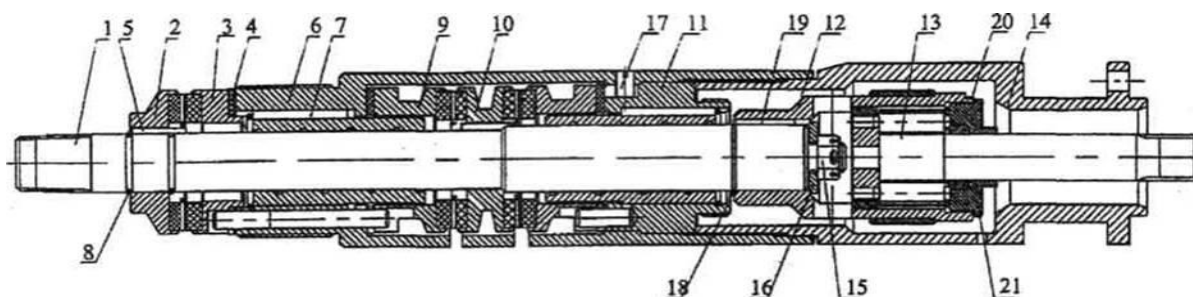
Основание: 1 - вал; 2 - обойма; 3 - обойма; 4 - кольцо; 5 - шпонка; 6 – корпус основания; 7 - шпонка; 8 – кольцо запорное; 9 - обойма; 10 - пята; 11 - вкладыш; 12 - полумуфта; 13 – муфта пусковая; 14 - переводник; 15 - гайка; 16 - шайба; 17 – винт стопорный; 18 – кольцо запорное; 19 - шпонка; 20 - кольцо; 21 - крышка;
